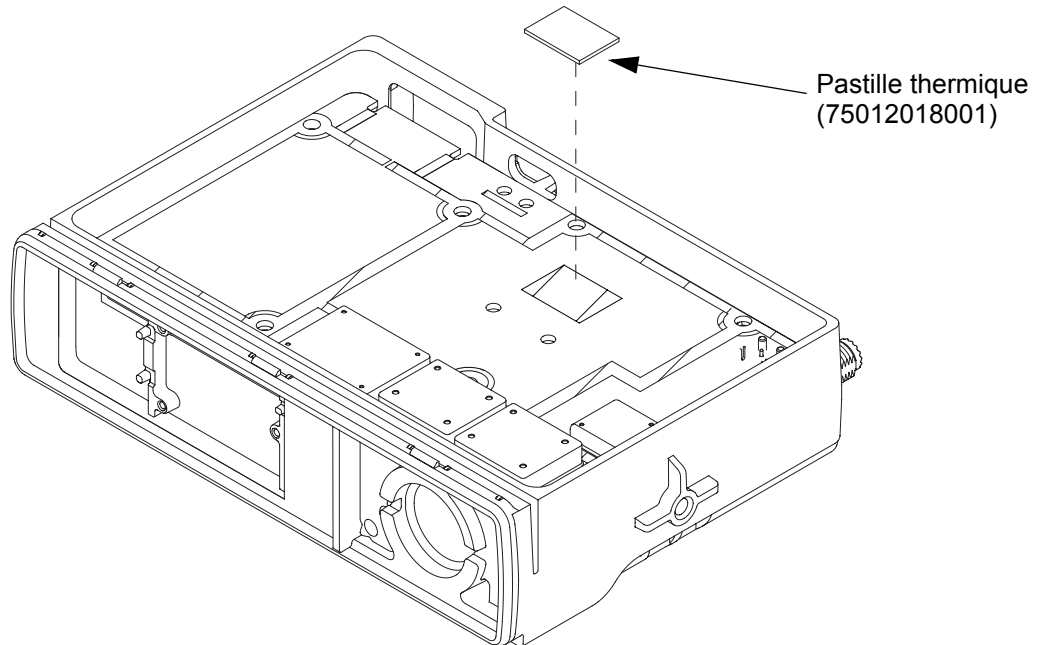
Remplacement de la carte thermique de la carte à circuit imprimé
